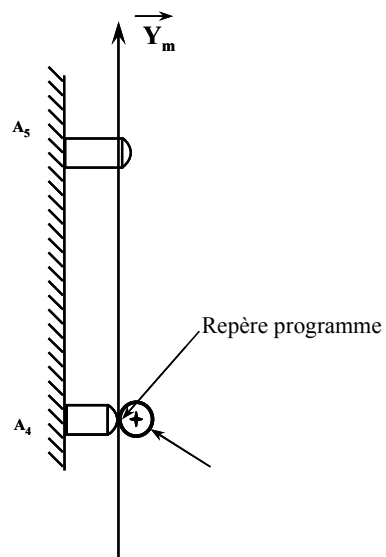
Construction du plan (\vec{Y}_m, \vec{Z}_m)
